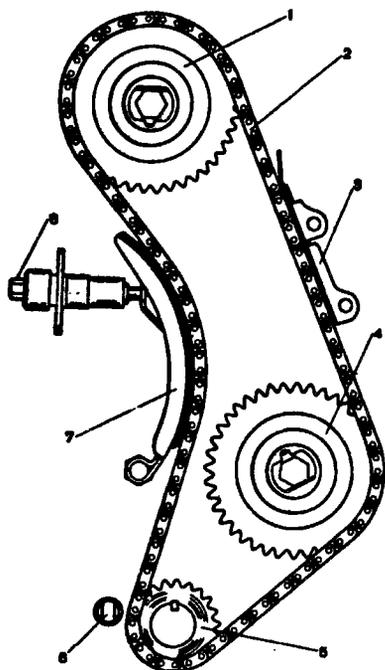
Схема механизма привода распределительного вала и вспомогательных органов: 1 - звездочка распределительного вала; 2 - цепь; 3 - успокоитель цепи; 4 - звездочка валика привода масляного насоса; 5 - звездочка коленчатого вала; 6 - ограничительный палец; 7 - башмак натяжителя; 8 - натяжитель цепи
